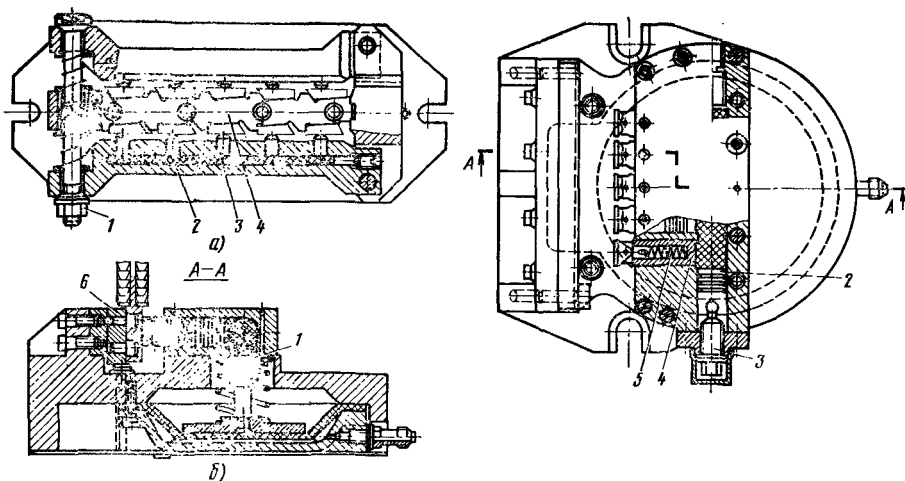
Приспособления для группового закрепления заготовок с гидропластмассой в качестве передаточного звена
